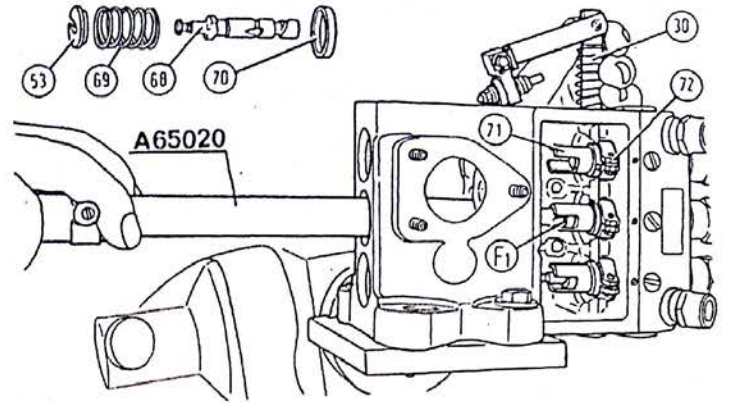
/27 - Montage (démontage) des pistons (68) au moyen de l'outil A 65020.
